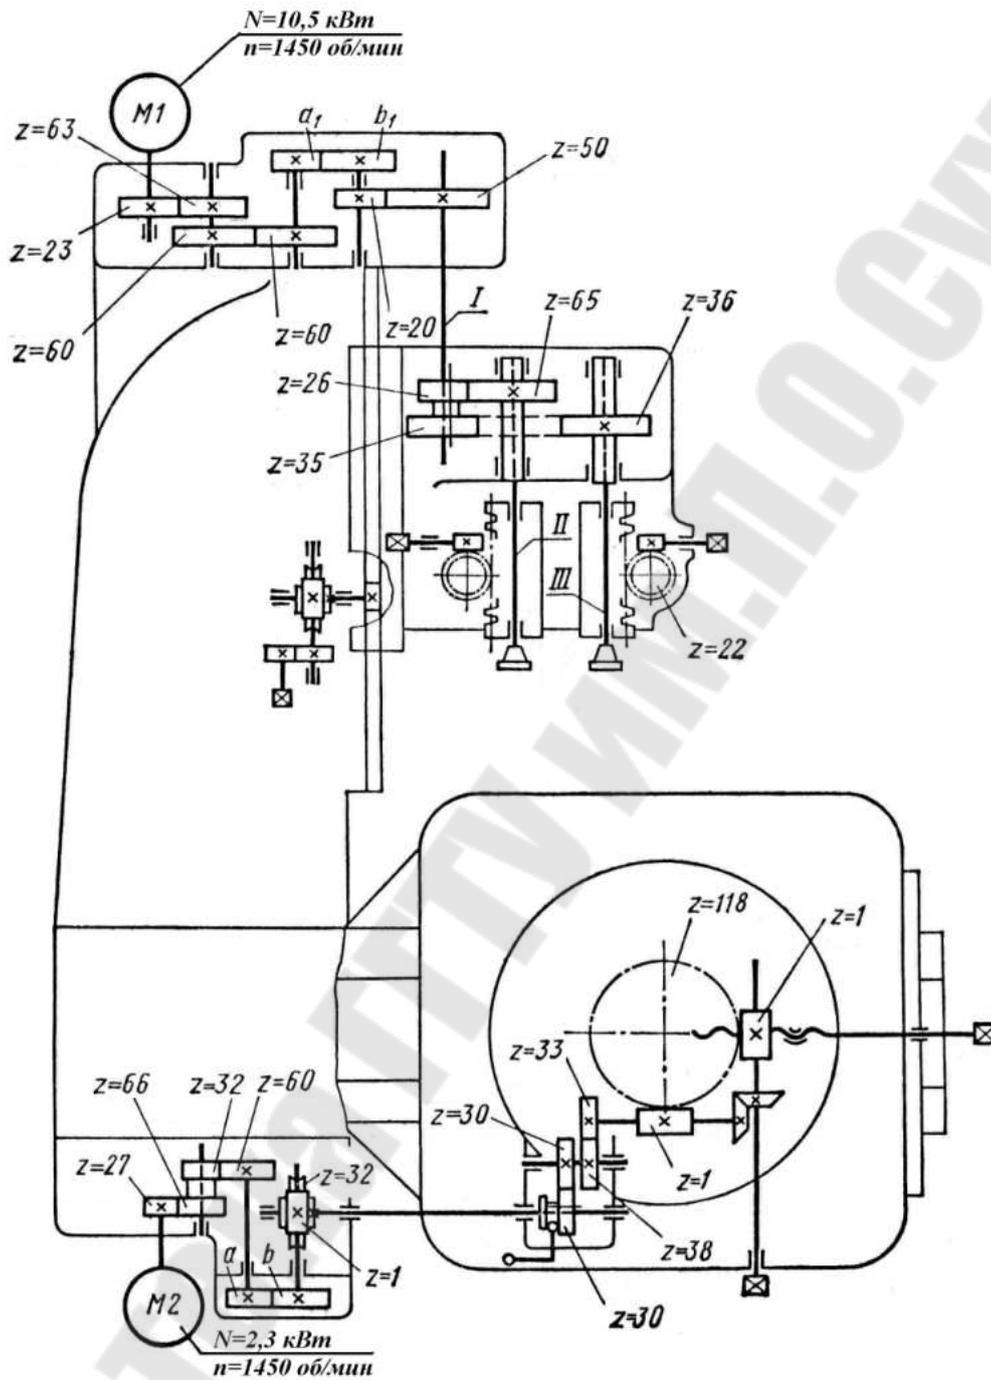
Кинематическая схема карусельно-фрезерного станка 6М21
